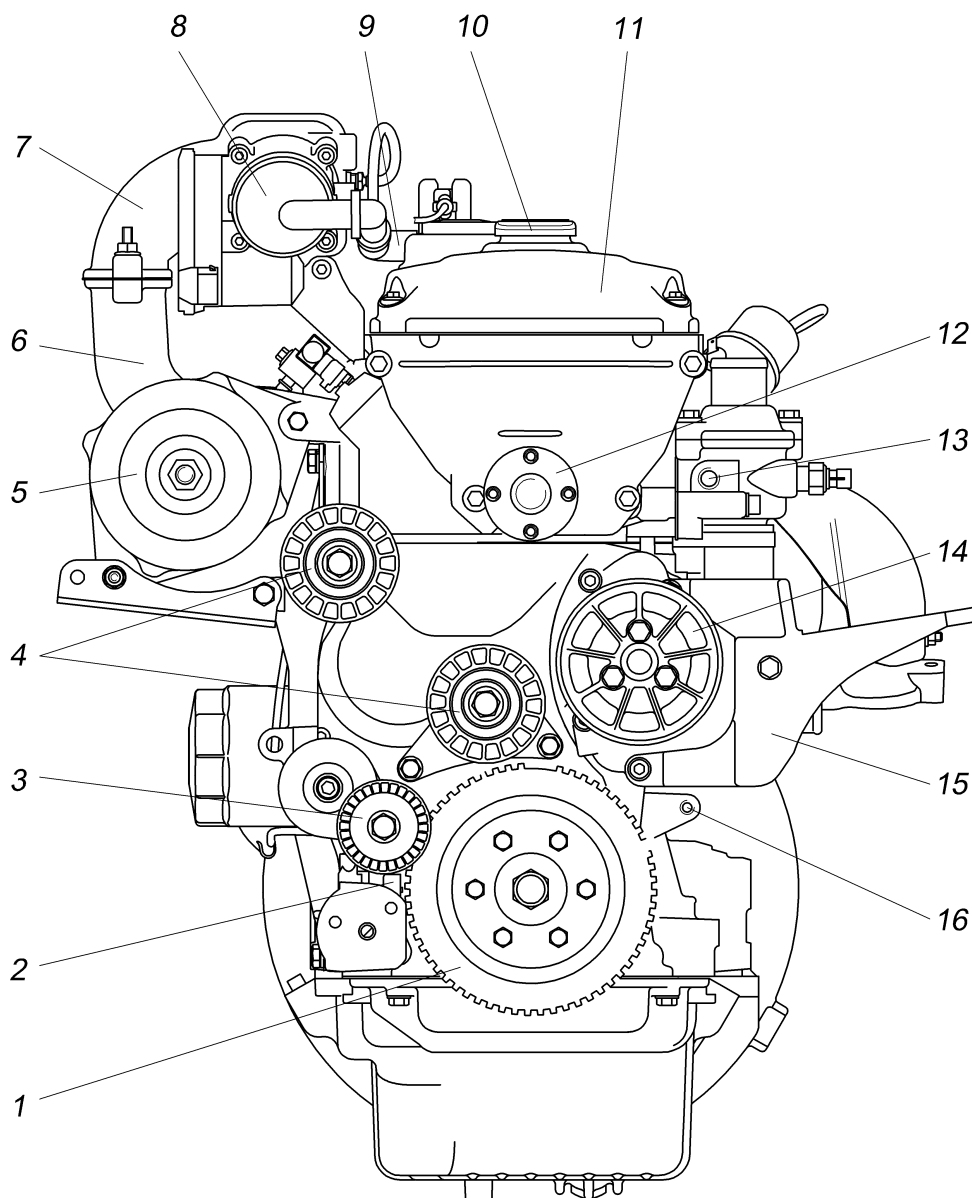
Вид спереди двигателя ЗМЗ-40904.10
